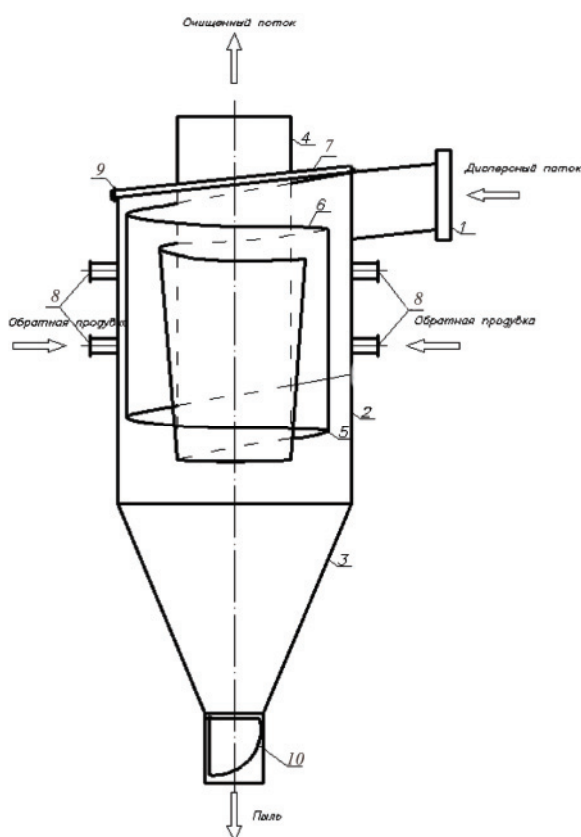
Схема конструкции циклона-фильтра: 1 – входной патрубок; 2 – цилиндрический корпус; 3 – коническое днище; 4 – выхлопная труба; 5 – фильтровальный материал; 6 – металлический каркас; 7 – торец циклона; 8 – продувочные штуцера; 9 – детали крепежа; 10 – заслонка
